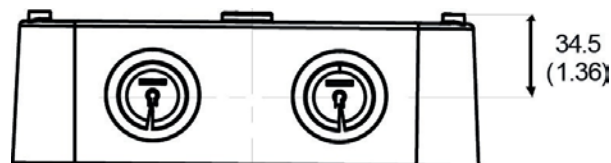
A52x kontrollen baksida Panel med Montage hål Dimensioner i Millimeter (Inches)
